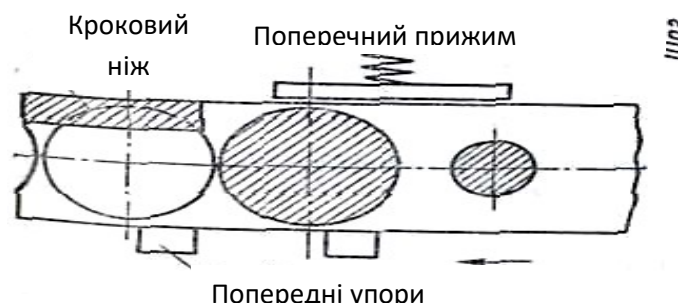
Розташування крокового ножа в відході смуги
